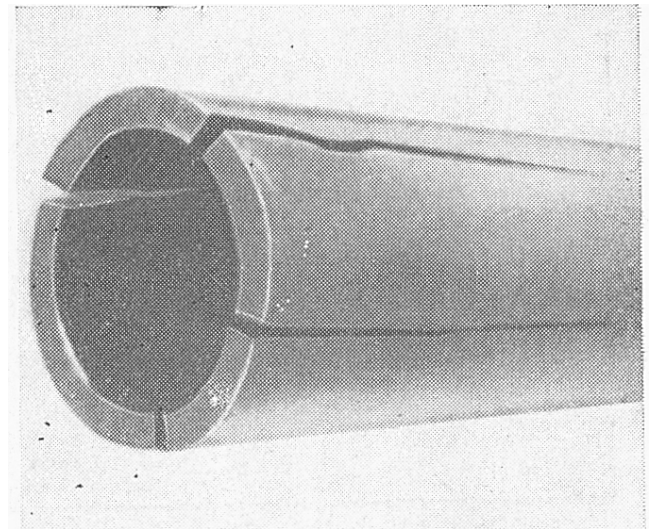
Трещины от остаточных напряжений в трубе из подшипниковой стали.
